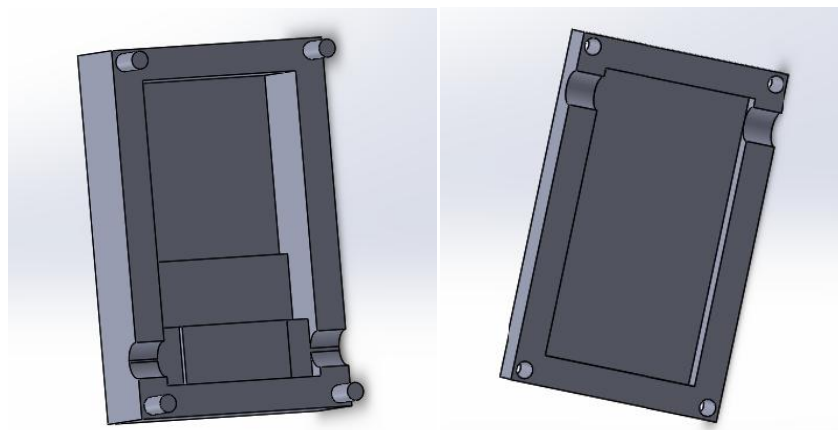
Desenho das partes inferior e superior do invólucro em 3D
